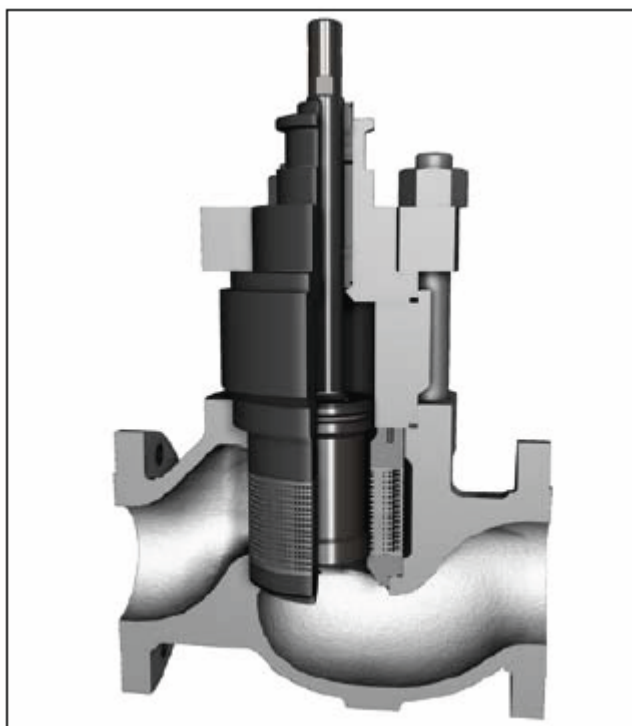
Клапан Mark One в сборе с затвором Stealth
